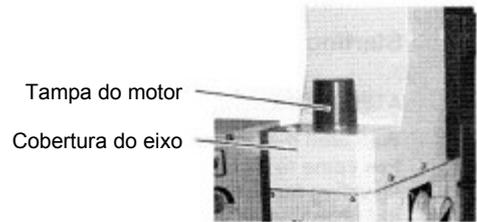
Cabeça de fresagem-furação ferramenta.
